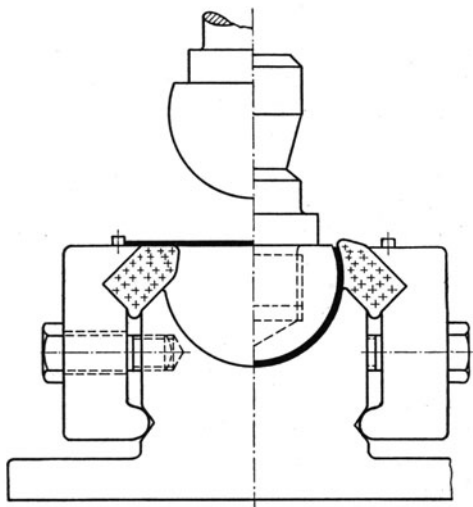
Gummibestücktes Anbiegewerkzeug für halbrunde Schalen zum Ausgleich der Rückfederung
